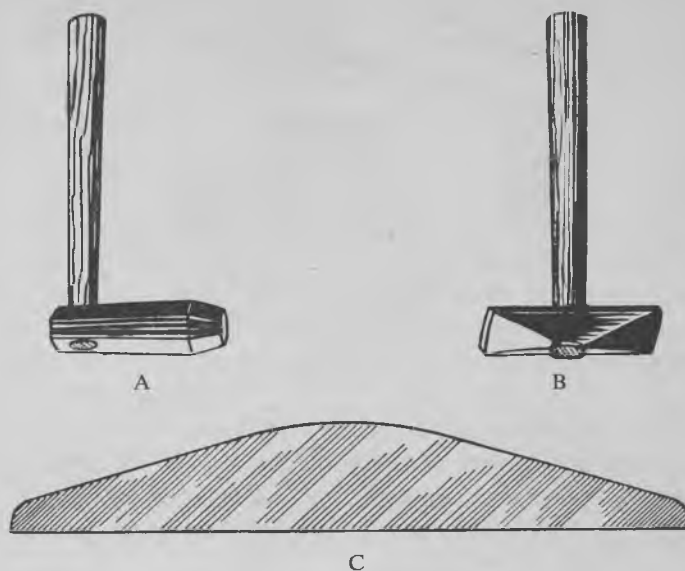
A: Rundhammer. B: Planhammer. C: Lineal.
